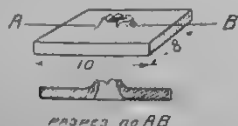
Изготовление фибровых (или прессшпановых) прокладок.
